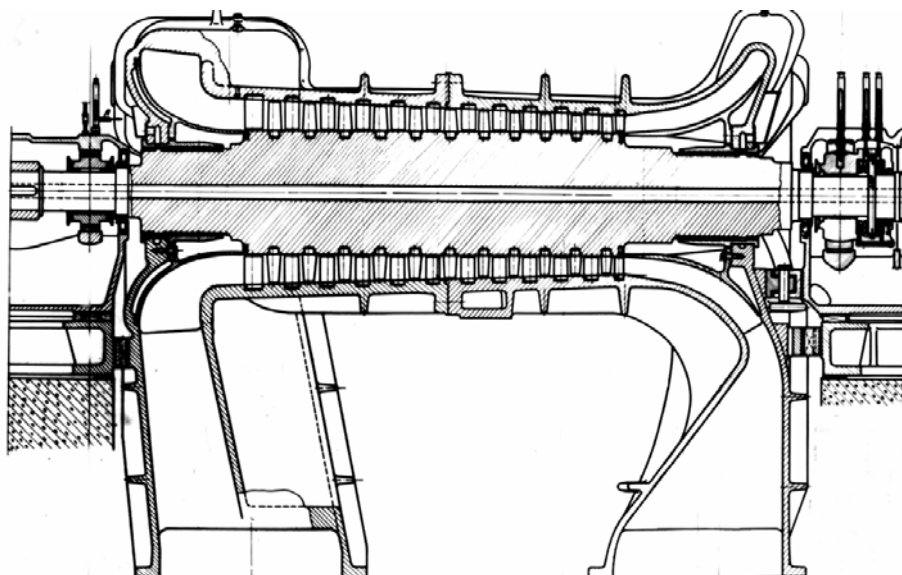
Компрессор высокого давления ГТ-700-12 (Невский Завод). Ротор барабанного типа из цельной поковки
